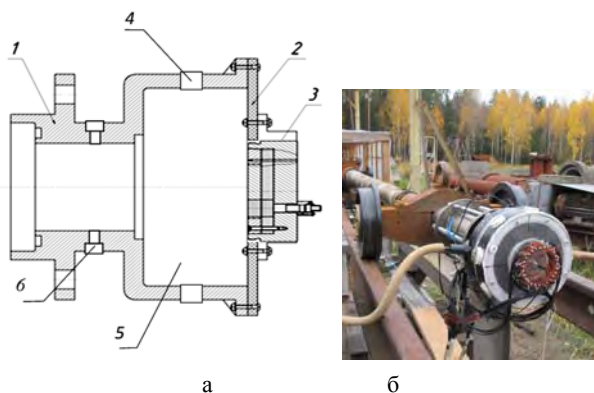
Надульный отсек: а – схема, б – внешний вид; 1 – корпус измерительного отсека; 2 – разрушаемое дисковоснование; 3 – нагружаемый блок с мишенью-образцом; 4 – отверстия для сброса газов; 5 – расширительная камера; 6 – отверстия для установки пьезоэлектрических датчиков давления и пусковых электроконтактов
